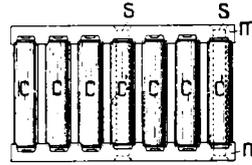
Rollenbefestigungs-Ringe, aufgerollt.
